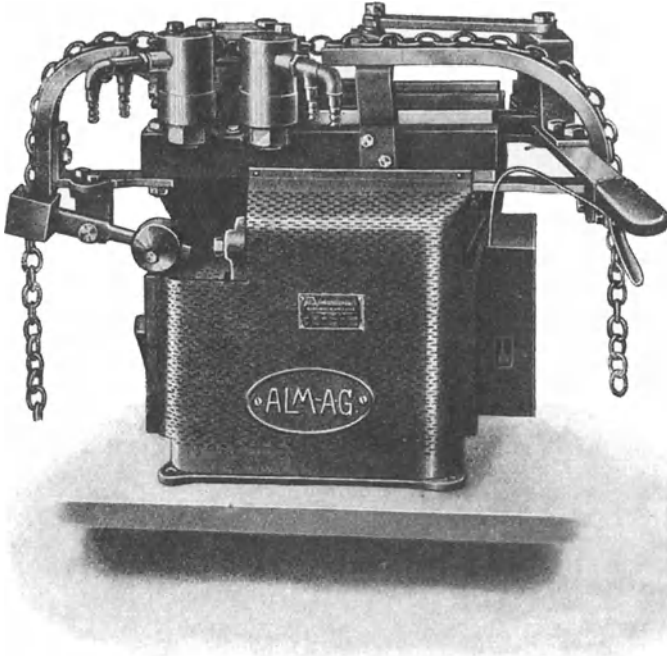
Tisch-Kettenschweißmaschine.
